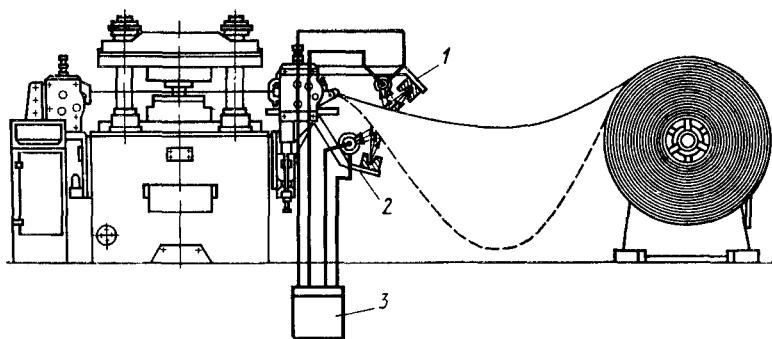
КБУ для управления двигателем разматывающего устройства
